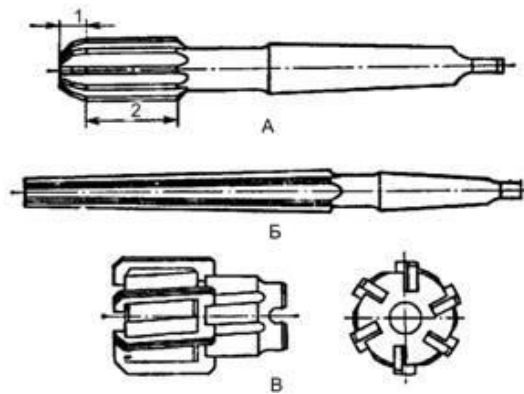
Розгортки: А- циліндрична; Б конічна;
